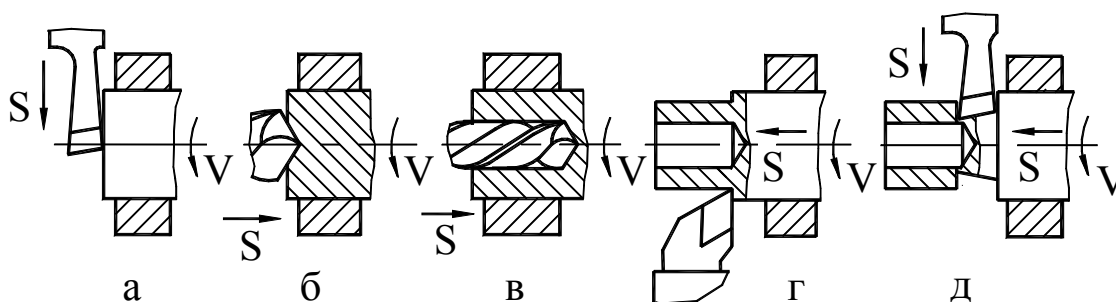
Обработка заготовки на автомате фасонно-продольного точения: а – подрезка торца, б – сверление отверстия, в – рассверливание отверстия, г – точение конуса, д – отрезка детали
